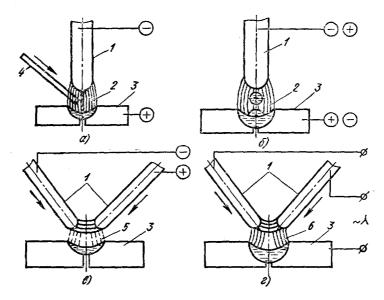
Сварка неплавящимся электродом (а); сварка плавящимся электродом (б); сварка дугой косвенного действия (в); сварка трехфазной дугой (г).
